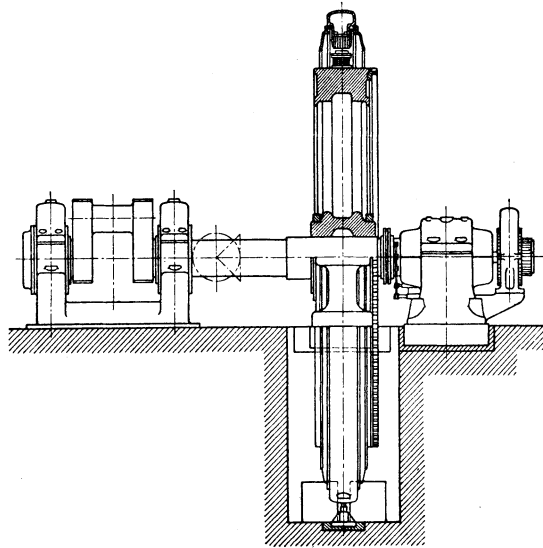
Drehstrom-Schwungradgenerator mit Schaltkranz für Gasmotorenantrieb.
